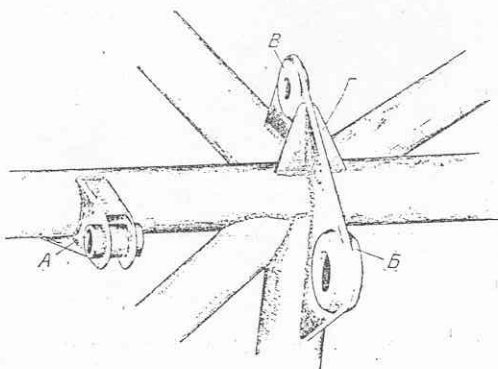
Верхний боковой узел рамы 3—4 (левый)
